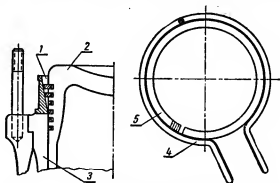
Приспособления для опускания поршня с кольцами в цилиндр:
